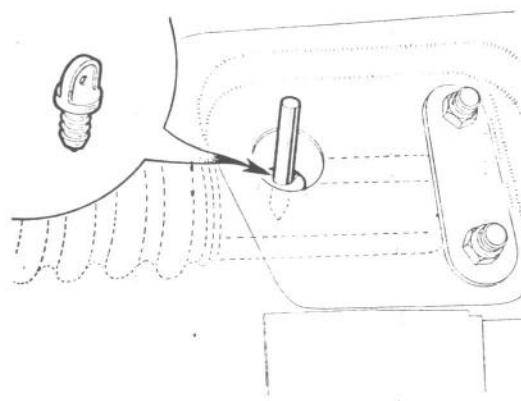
Colocación de un pasador o tornillo para centrar la cremallera, durante el montaje de la columna de dirección.
